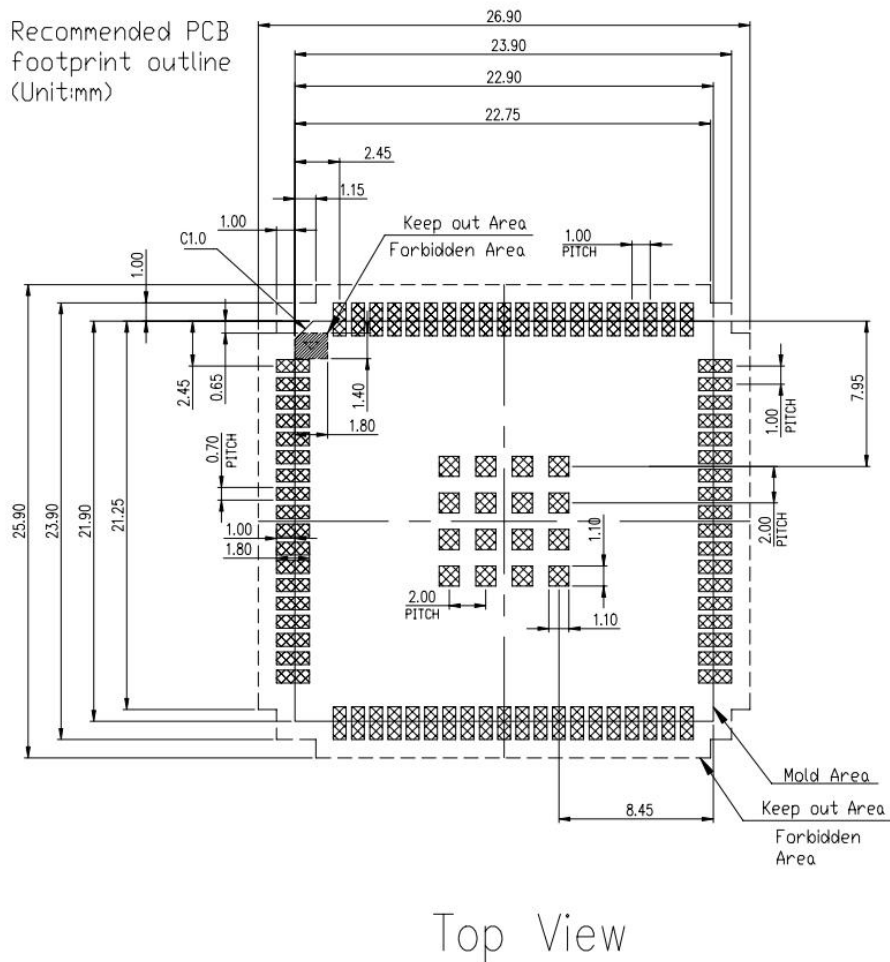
：推荐 PCB 封装尺寸（单位：毫米）（A7630C）
